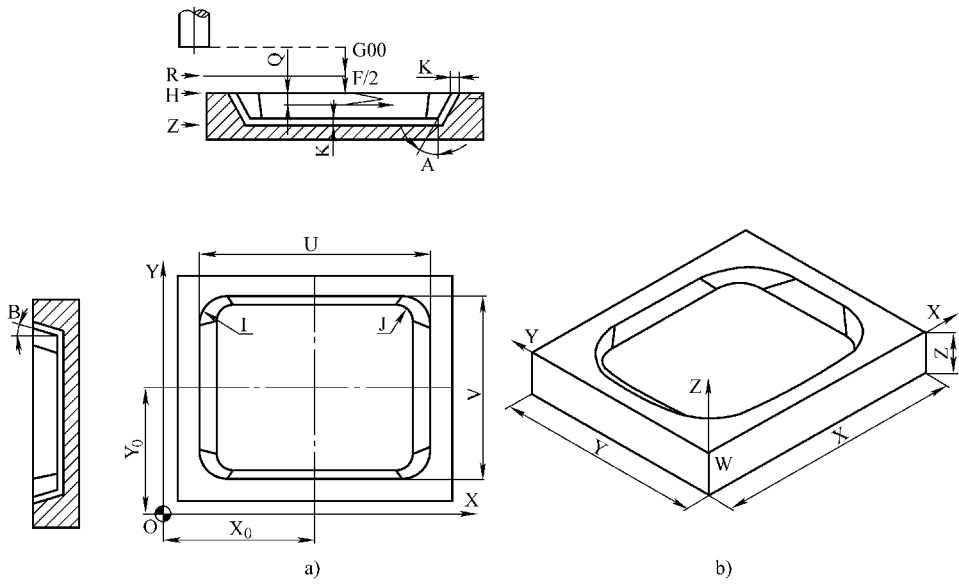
四方锥槽类零件侧面铣削刀具路线示意图
